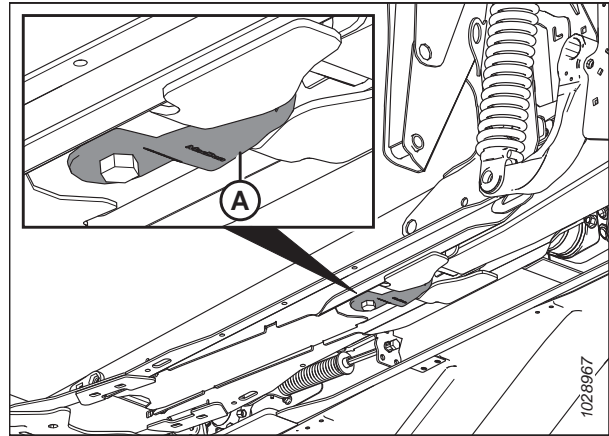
Piattaforma di alimentazione – Vista dal basso
